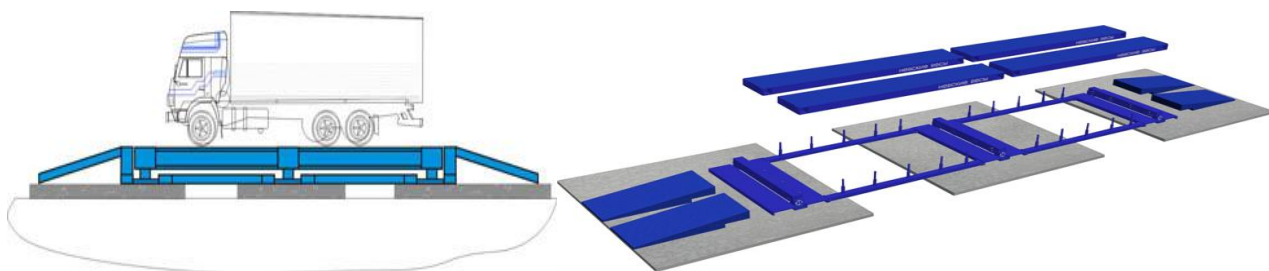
Загальний вигляд та платформа для зважування а статиці [6]
